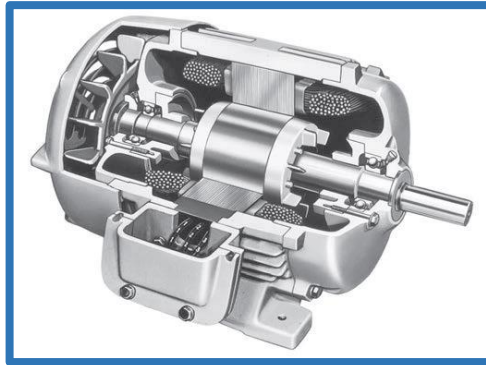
MOTOR DE INDUCCIÓN ELÉCTRICA. FUENTE [20]
